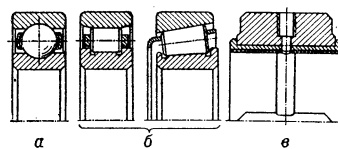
Подшипники: а — шариковый; б — роликовые цилиндрический и конический; в — скольжения.
